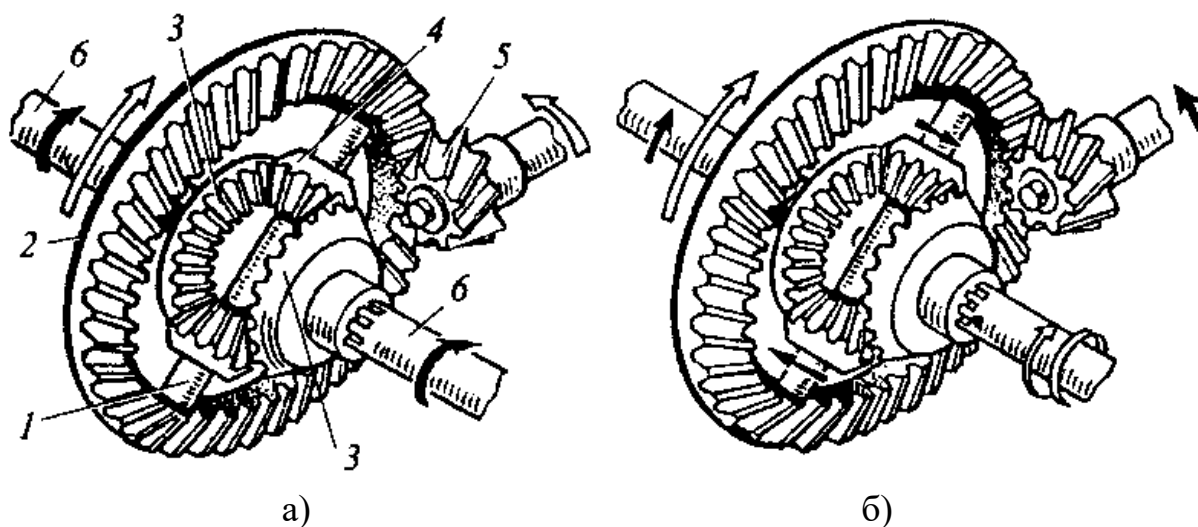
Будова і принцип роботи диференціала: а - рух по прямій; б - рух при повороті: 1 - вісь сателітів; 2 – ведена шестерня; 3 - півосьова шестерня; 4 - сателіти; 5 - ведуча шестерня; 6 - піввісь.
